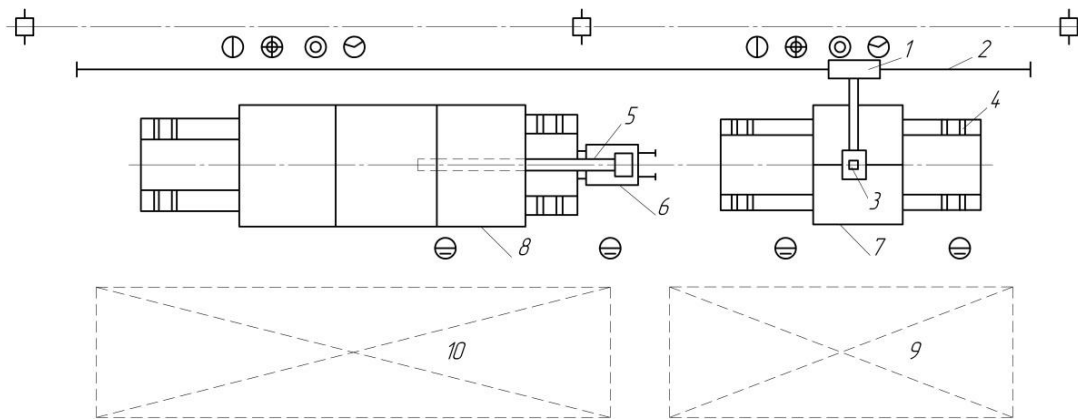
Планировка участка сборки и автоматической дуговой сварки под флюсом цилиндрических изделий:
